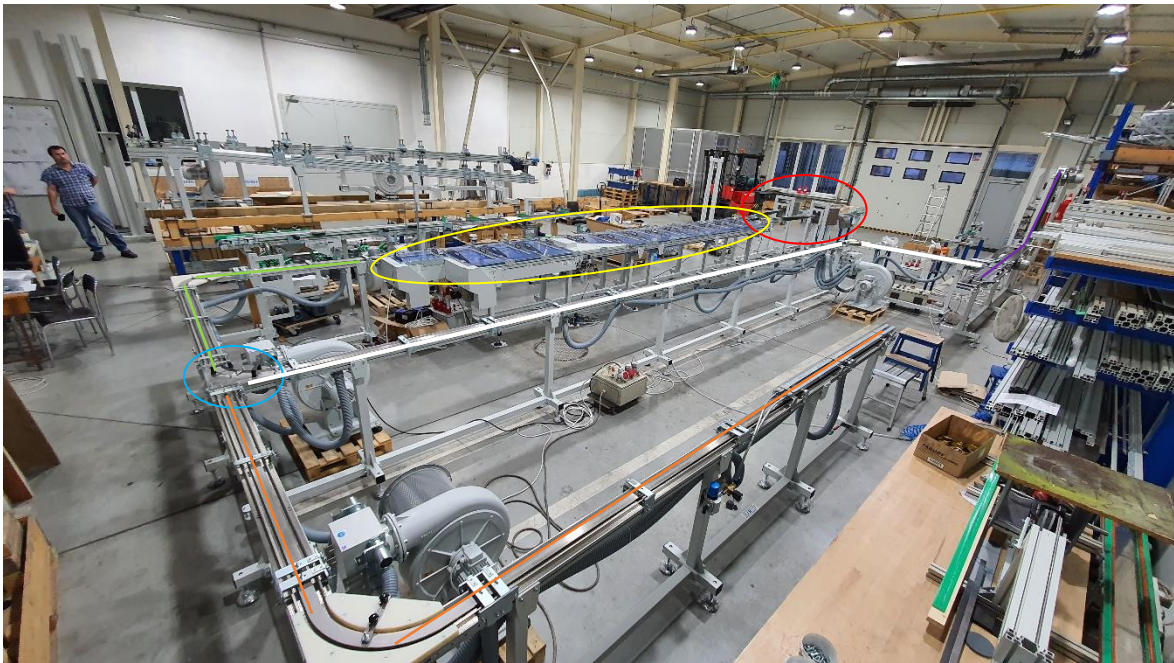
90° zatáčka JET dopravniku se směrovými tryskami [Autor]
